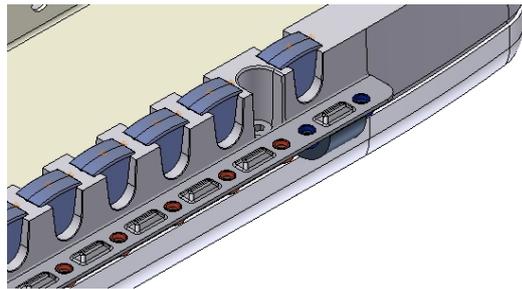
Unbenutzte Kabeldurchgänge abgedichtet
